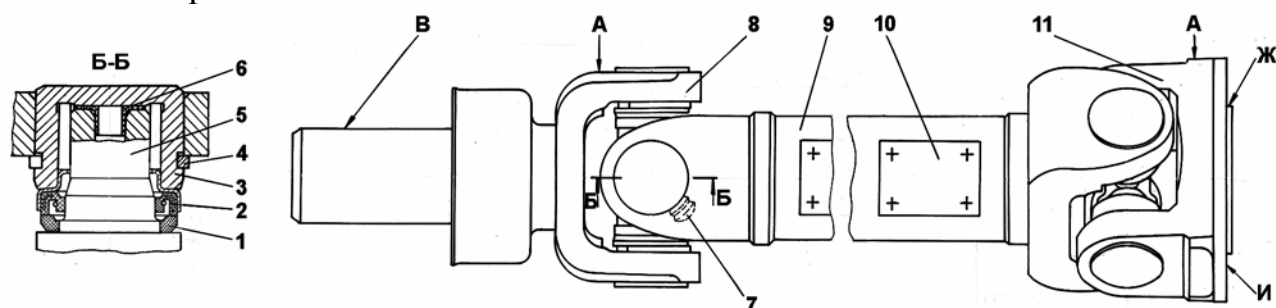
Промежуточный карданный вал: А – места допустимых ударов при разборке; 1 – отражатель; 2 – манжета; 3 – игольчатый подшипник; 4 – стопорное кольцо; 5 – крестовина; 6 – торцовая шайба; 7 – пресс-масленка с колпачком; 8 – скользящая вилка; 9 – труба; 10 – балансировочная пластина; 11 – фланец
